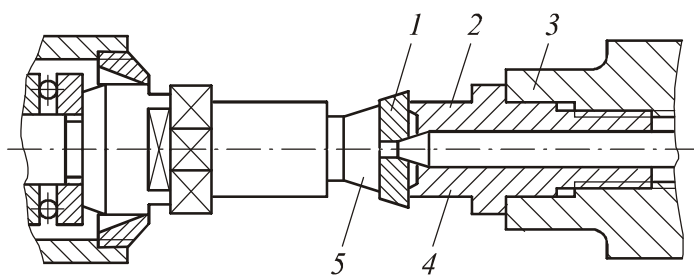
Схема базирования пластины по отверстию: 1 – пластина; 2 – шток; 3 – шпиндель изделия; 4, 5 – зажимные цапфы
